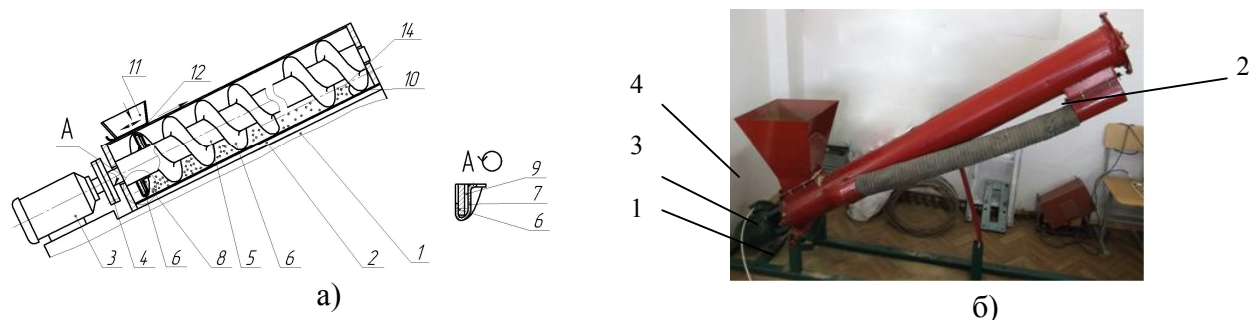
Гвинтовий конвеєр а) принципова схема; б) загальний вигляд експериментальної установки
